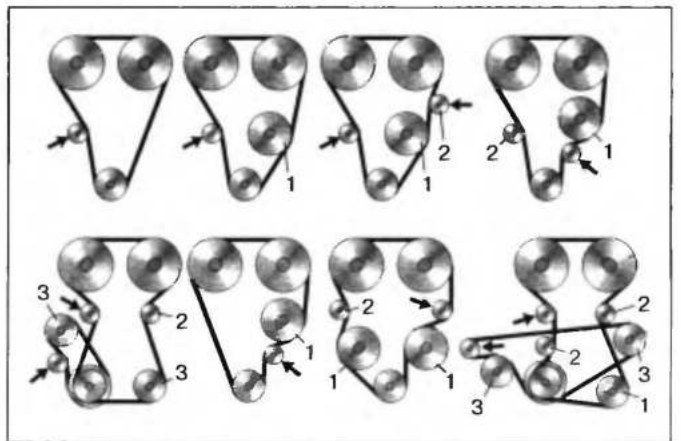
Основные схемы ременного привода распределительного механизма с двумя верхними валами: 1 — шкив привода вспомогательных агрегатов; 2 — паразитный ролик; 3 — шкив балансирного вала
